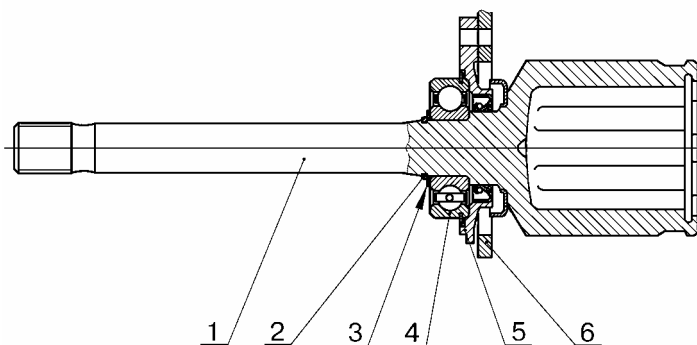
Корпус внутреннего шарнира 2121/21215-2215060/61 в сборе:
